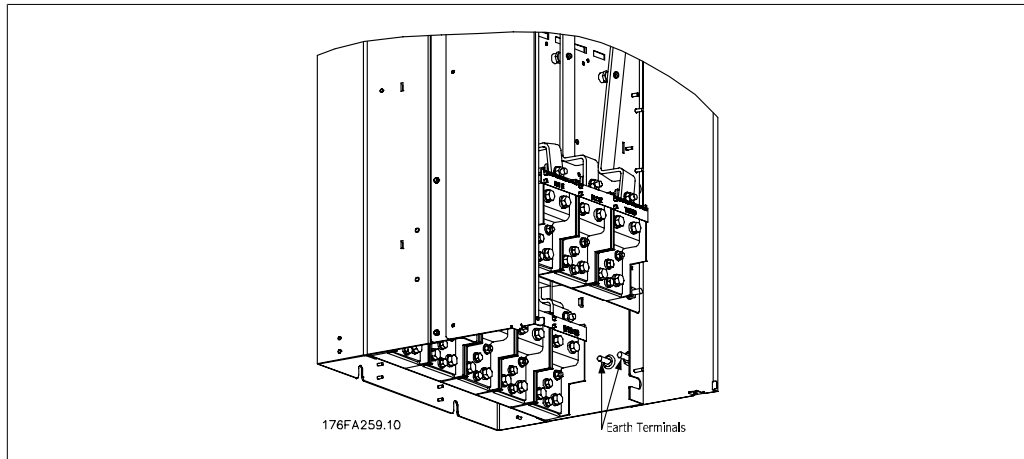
Расположение клемм заземления, IP00, корпуса E
